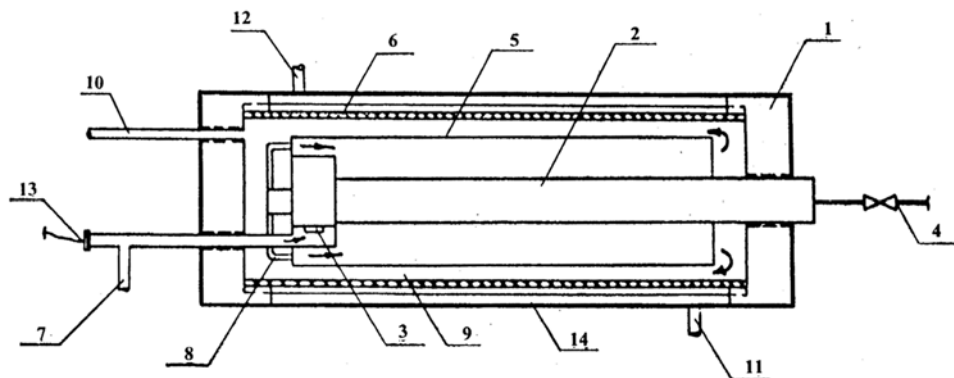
Высокочастотный генератор озона: 1 – корпус; 2 – высоковольтный электрод – вихревая труба; 3 – сопловый ввод; 4 – трубопровод отвода горячего воздуха; 5 – газонаправляющий кожух; 6 – низковольтный электрод; 7 – патрубок ввода подготовленного газа; 8 – патрубки холодного воздуха; 9 – разрядная камера; 10 – патрубок отвода озono-воздушной смеси; 11, 12 – патрубки подвода и отвода охлаждающей жидкости; 13 – устройство подачи высокого напряжения; 14 – охлаждающая рубашка
